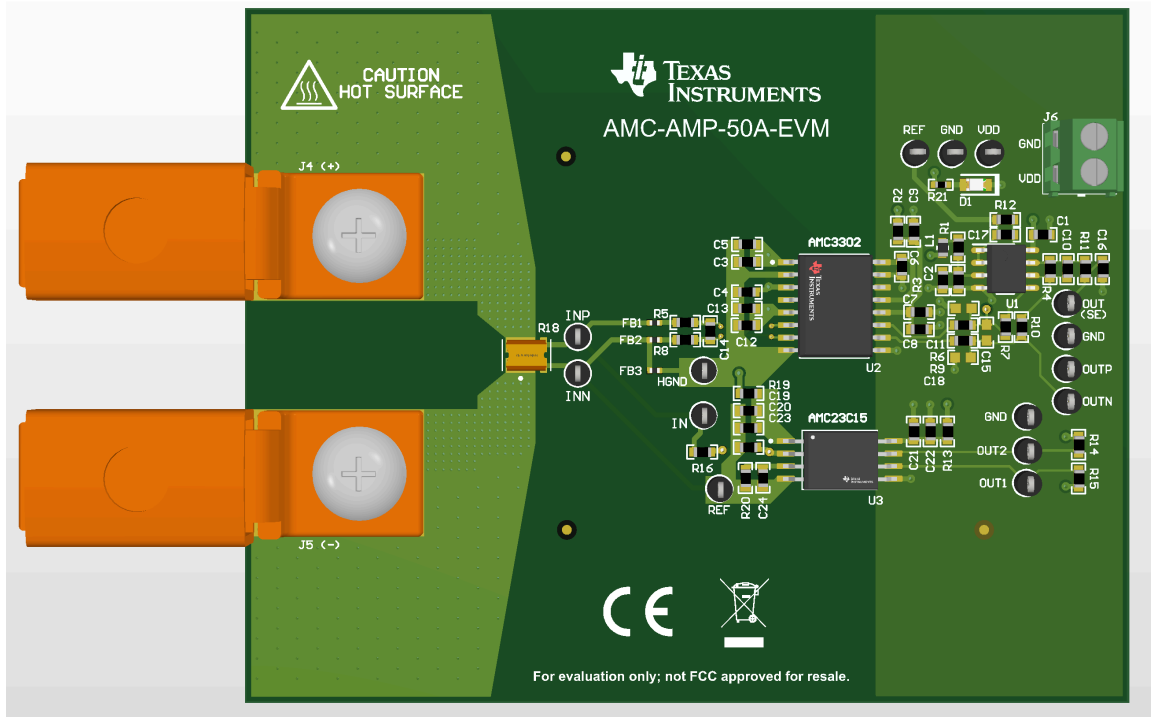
AMC-AMP-50A-EVM 顶部 PCB 图
